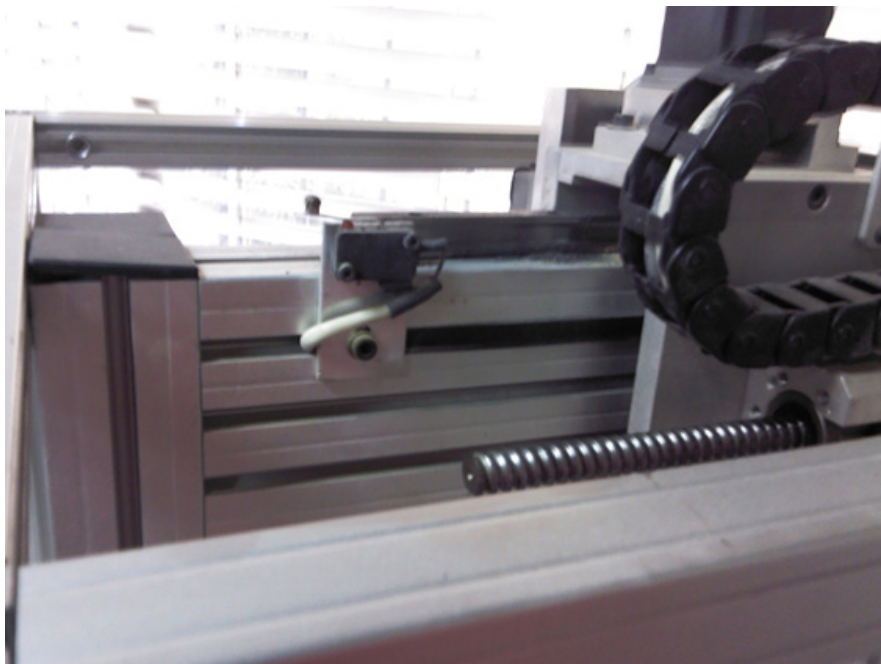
Esteira porta cabos montada sobre o carro do spindle.
